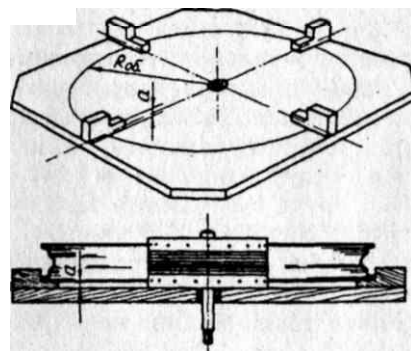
Приспособление для сборки колеса: а - величина выступления барабана за плоскость обода
